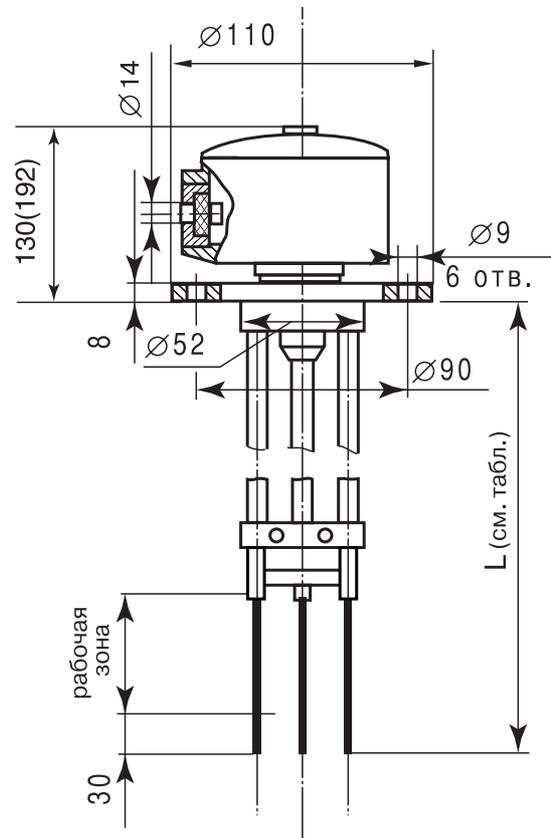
Общий вид, габаритные и установочные размеры СУС 161Р(Б)
